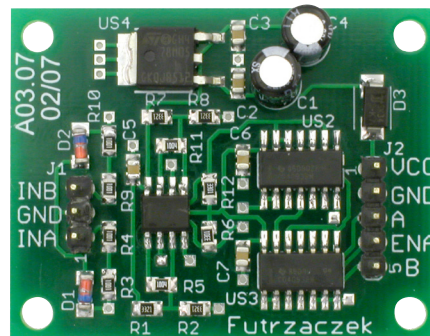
Schemat płytki PCB wraz z rozmieszczeniem elementów (skala 1:1)
